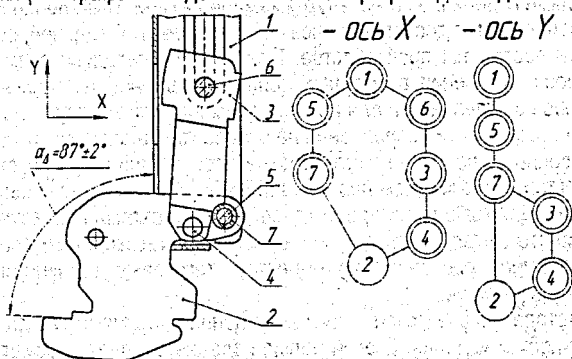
Эскиз сборочной единицы и графа деталей:
